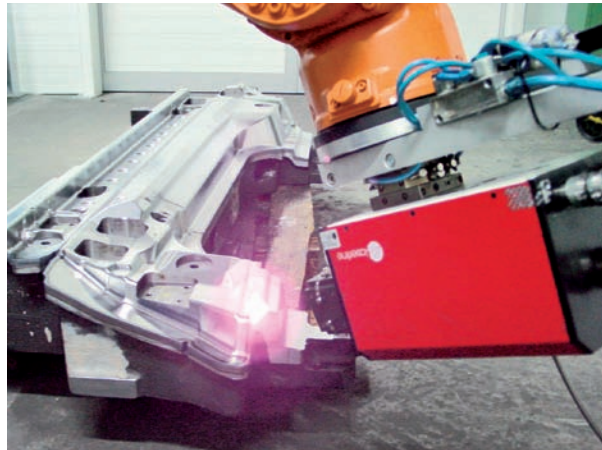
Laserstrahlgehärtete Segmente eines Schneidwerkzeugs
